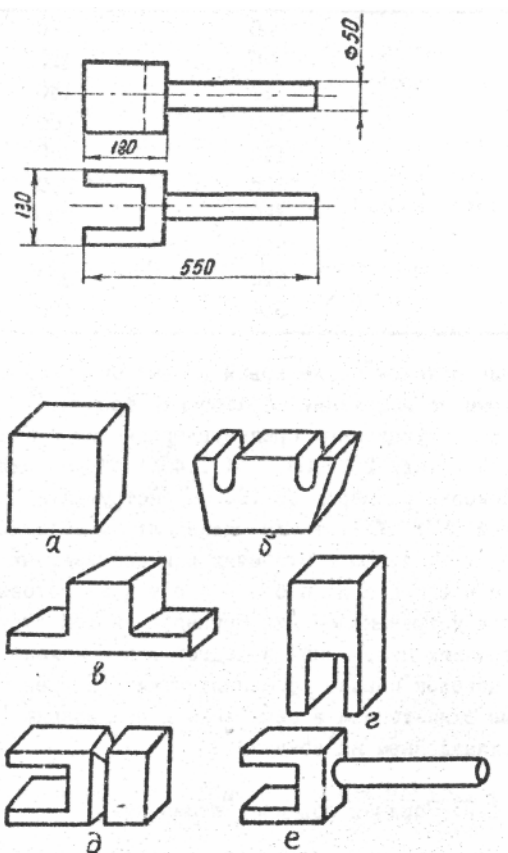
Переходы при ковке вилки из прямоугольной заготовки
